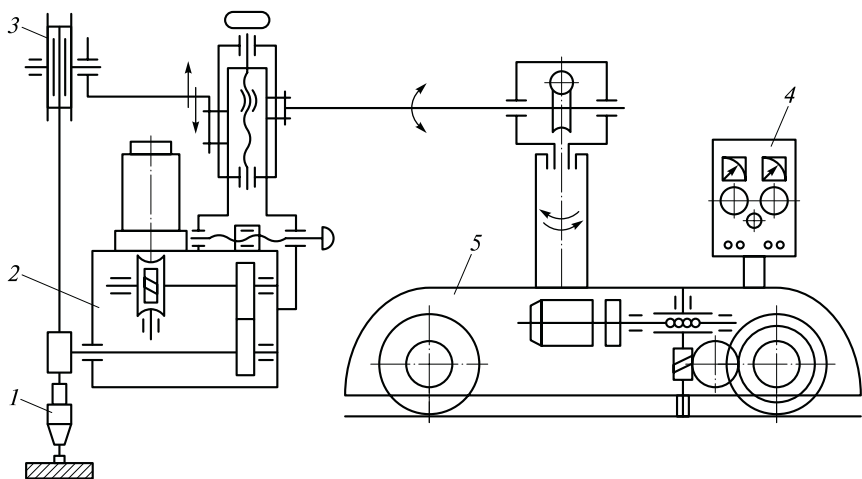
Схема сварочного трактора для сварки плавящимся электродом:
